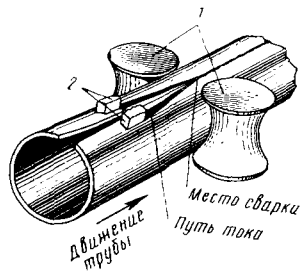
Схема контактной сварки труб током высокой частоты
